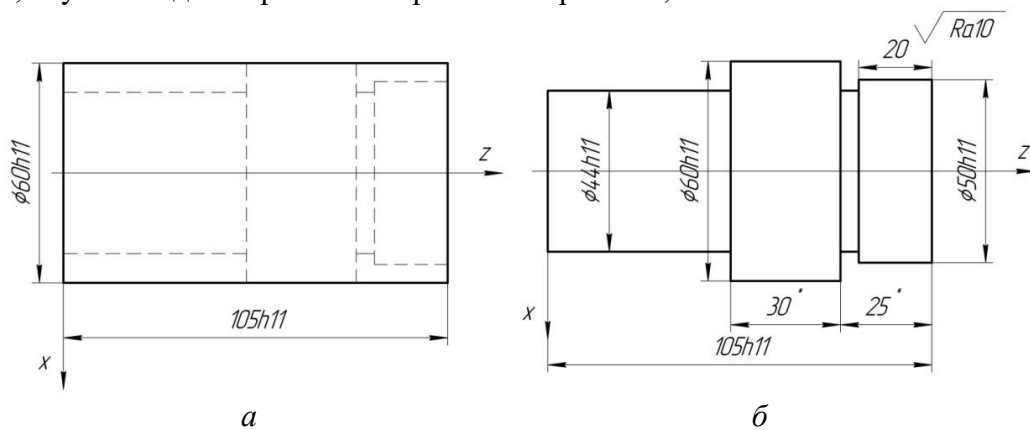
Ескіз заготовки (а) та деталі (б)
